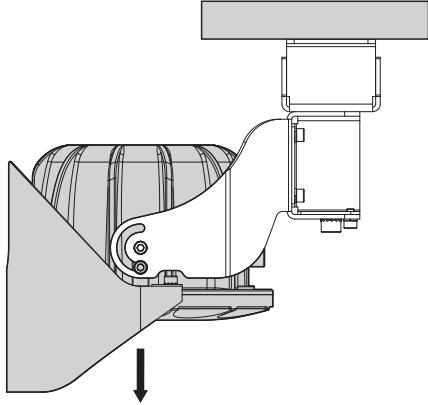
Монтаж на потолок (вертикальное перемещение, -90°).
